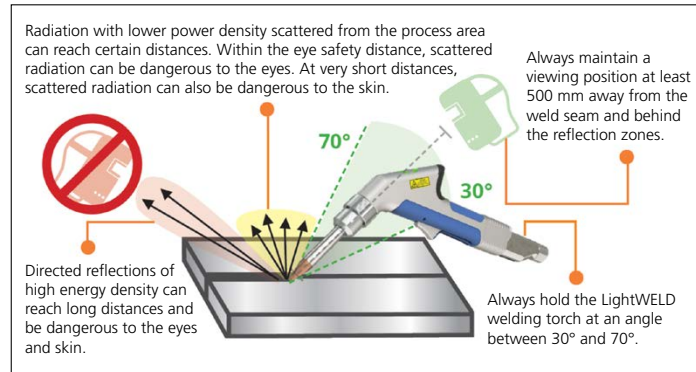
Empfohlene Strahlwinkel für das handgeführte Laserschweißen (mit freundlicher Genehmigung von IPG Laser GmbH & Co. KG, Deutschland)
